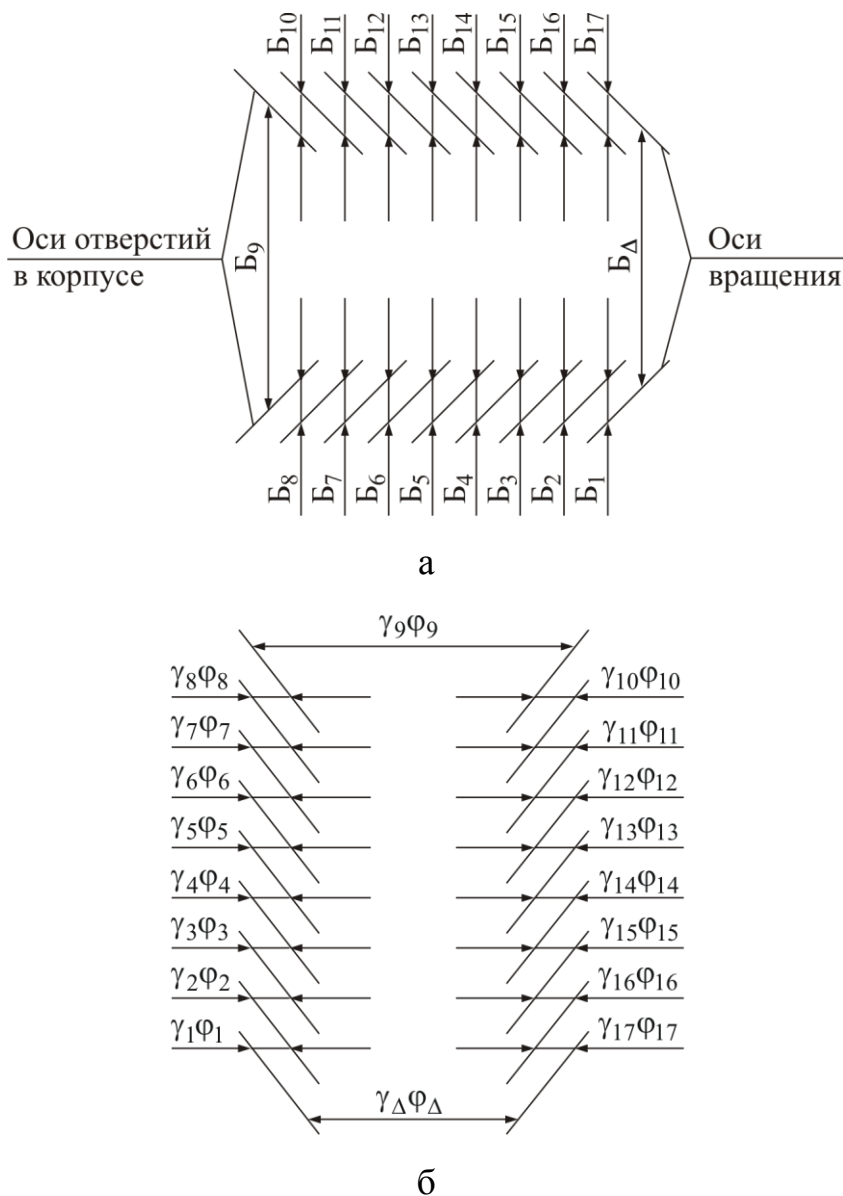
Схема сборочных размерных цепей одноступенчатого редуктора:
